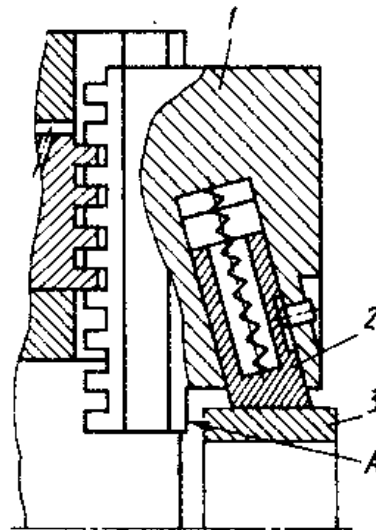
Автоматичний підтиск торця заготовки
